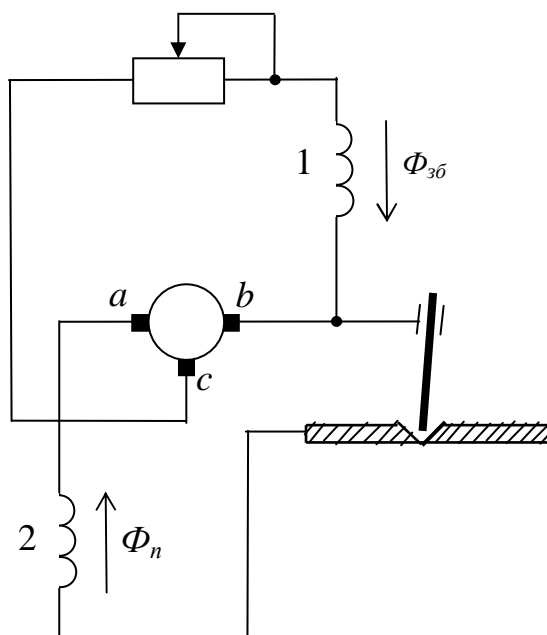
Зварювальний генератор з розмагнічуючою дією реакції якоря:
